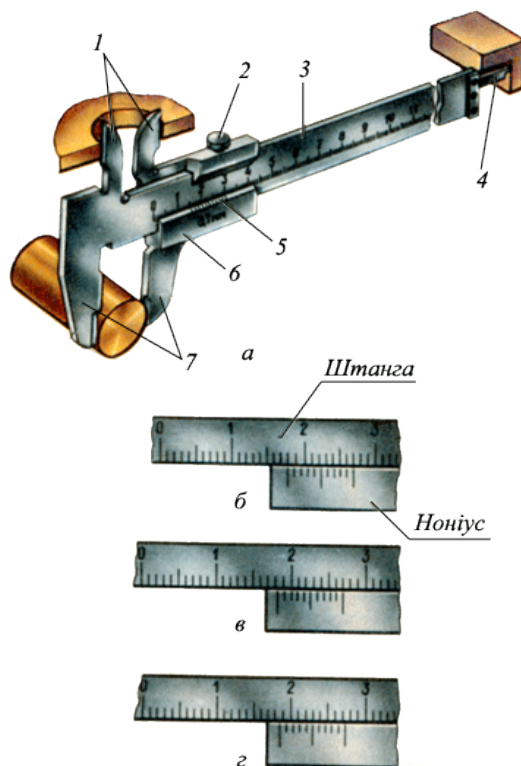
Штангенциркуль ШЦ –1: а – вимірювання елементів деталей штангенциркулем ШЦ –1; б – розмір вимірювальної величини 18 мм; в – розмір вимірювальної величини 18,2 мм; г – розмір вимірювальної величини 18,4 мм; 1 – губки для внутрішніх вимірювань; 2 – затиск; 3 – штанга; 4 – лінійка глибиноміра; 5 – шкала –ноніус; 6 – рамка; 7 – губки для зовнішніх вимірювань
